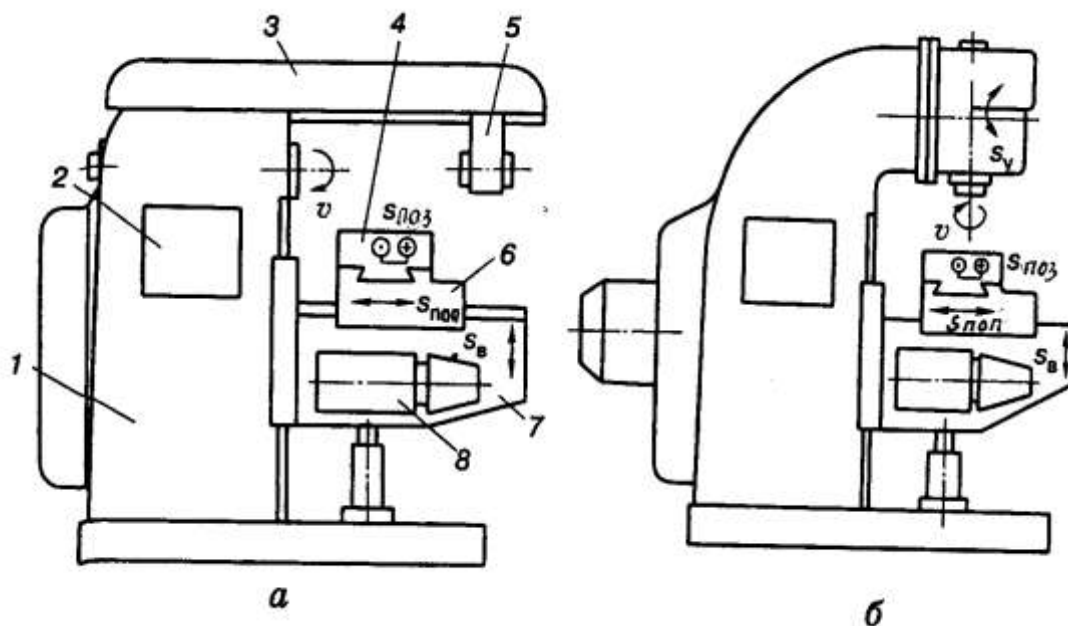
Консольні горизонтально-фрезерний (а) і вертикально-фрезерний (б) верстати
